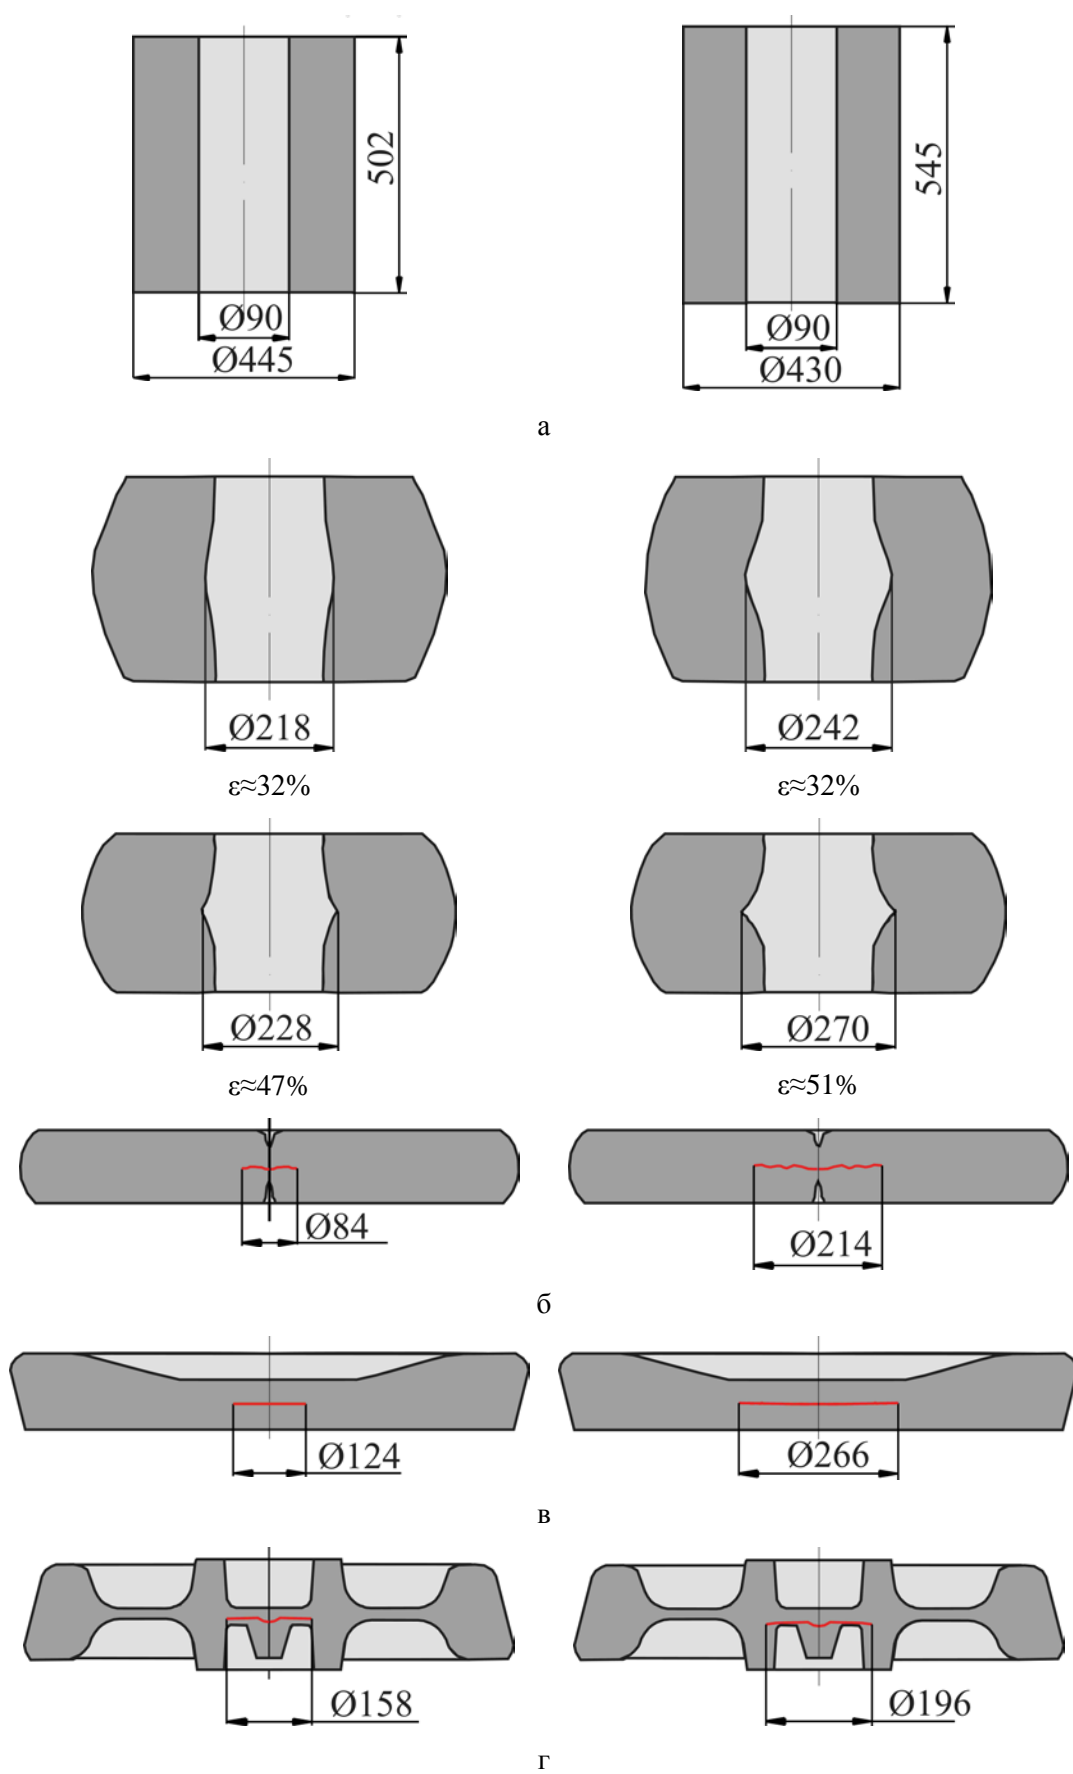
Формоизменение полый заготовки: а- исходная заготовка, б- свободная осадка, осадка и разгонка в кольце, г-формовка
